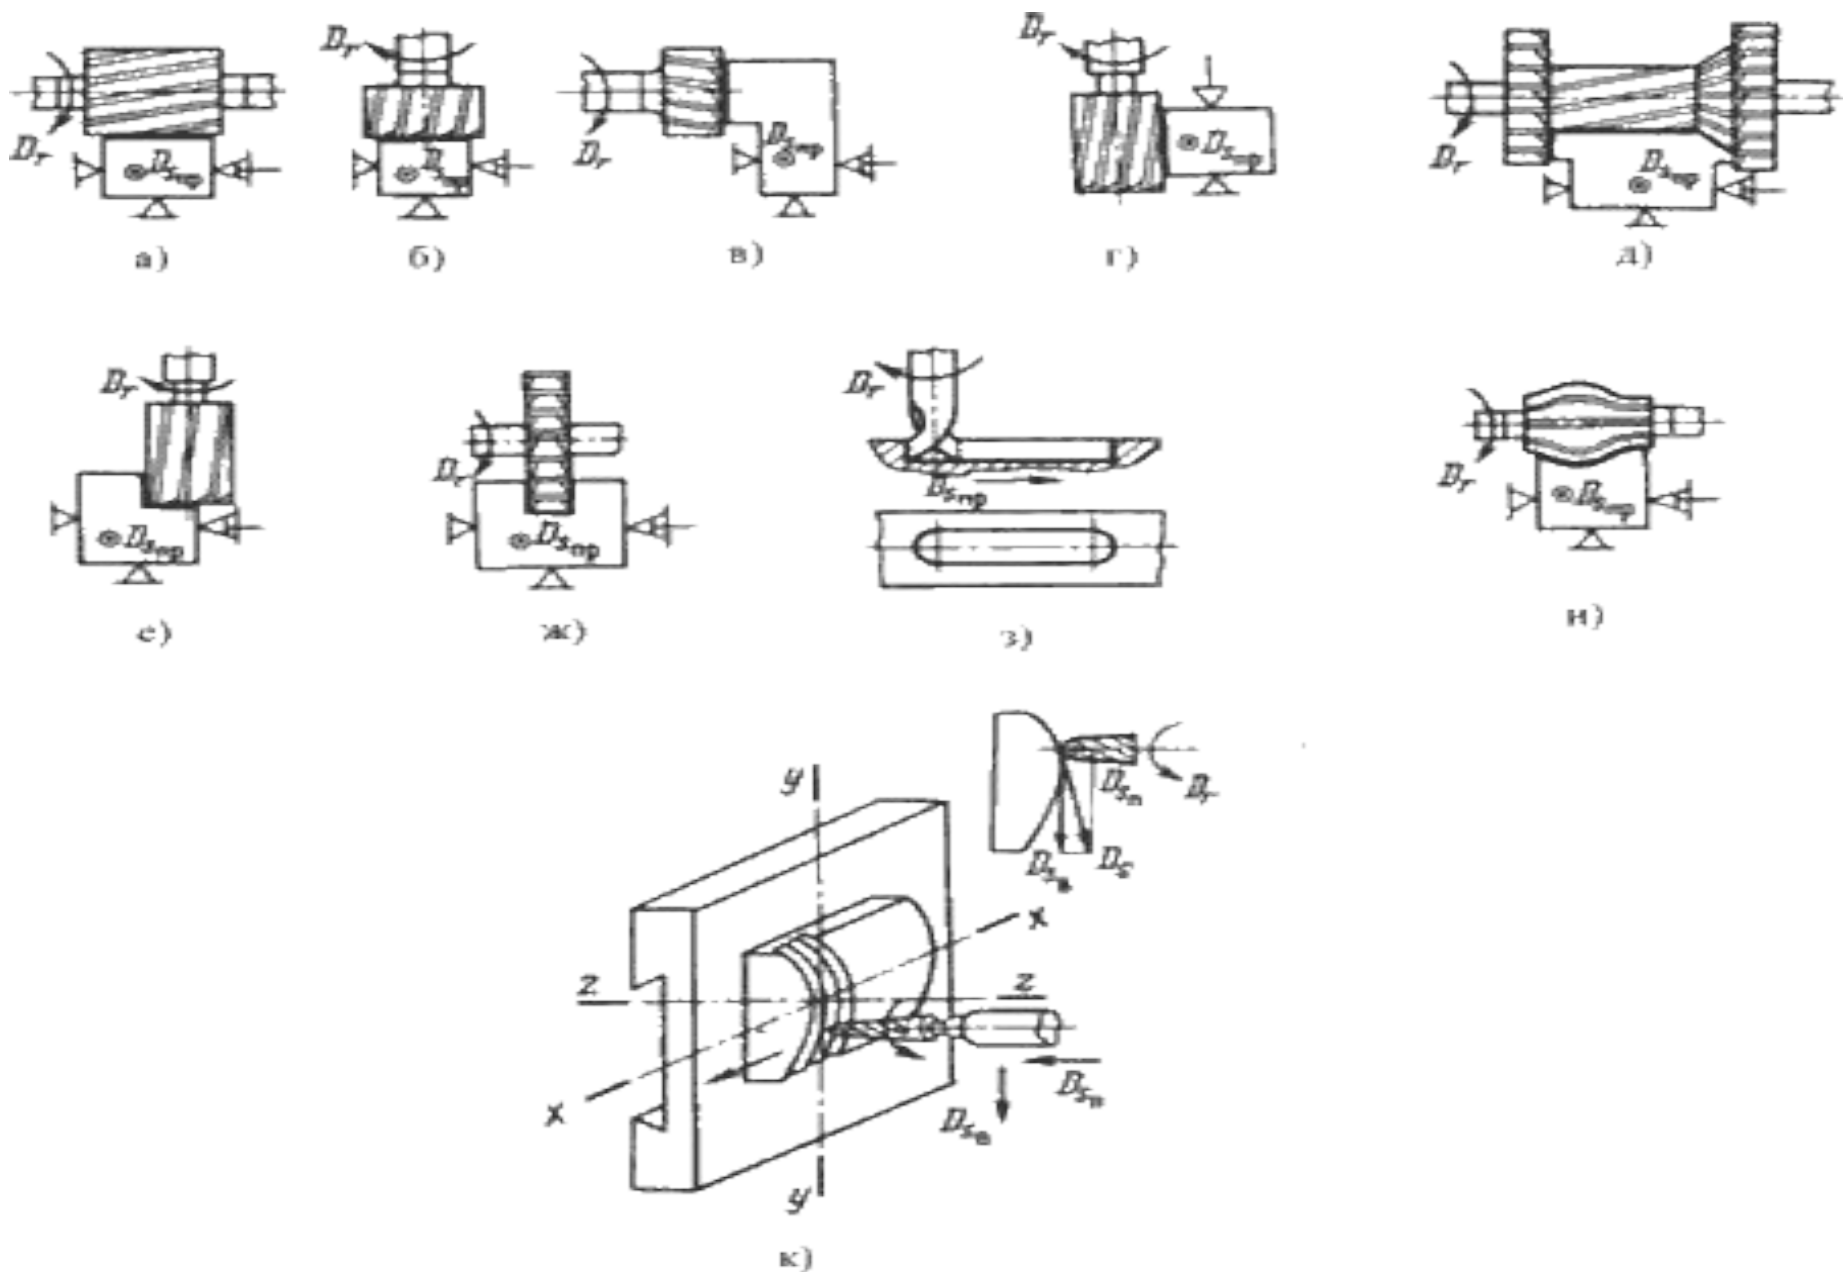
Схемы обработки заготовок на станках фрезерной группы
